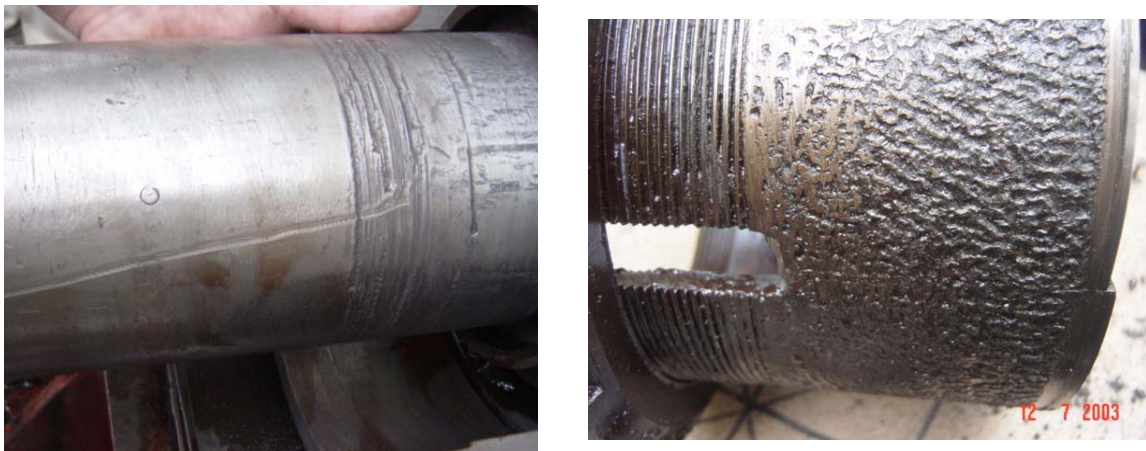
Ejemplo de eje dañado por soldadura severa en descanso
